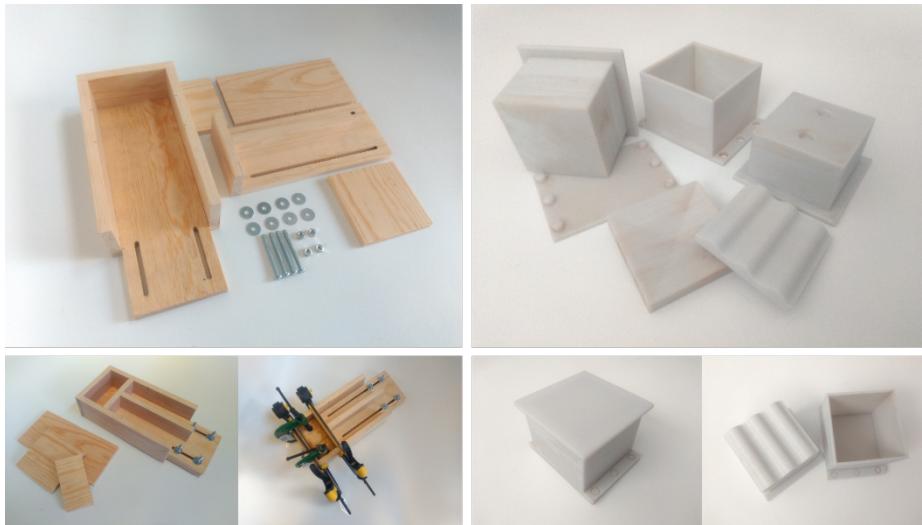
Moldes elaborados para la compresión y moldeo del material.
